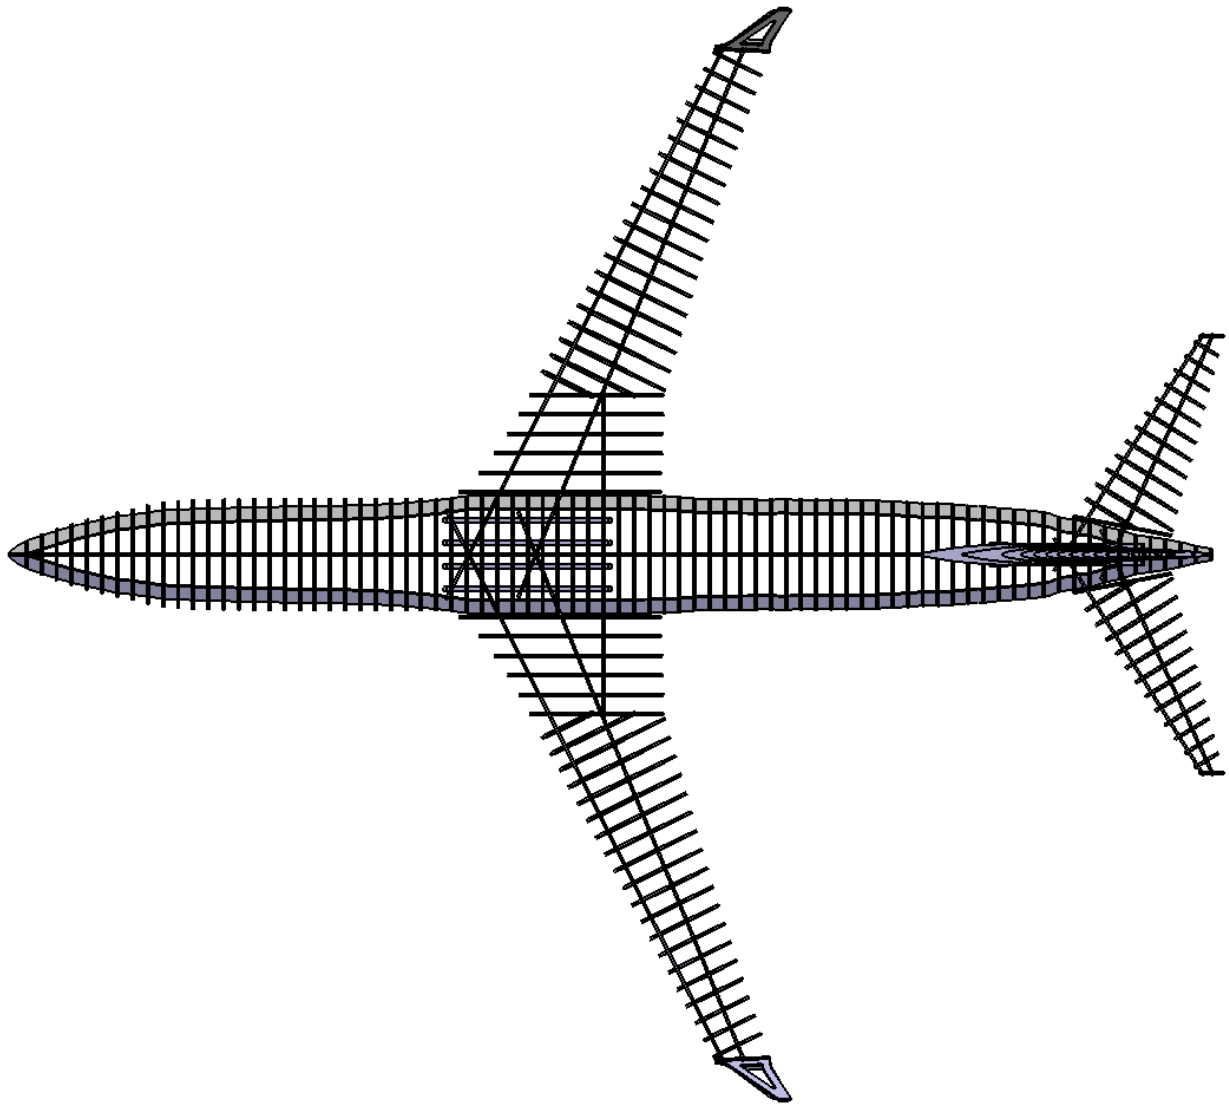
Vista en planta del disseny del Boeing 737-800 MAX
